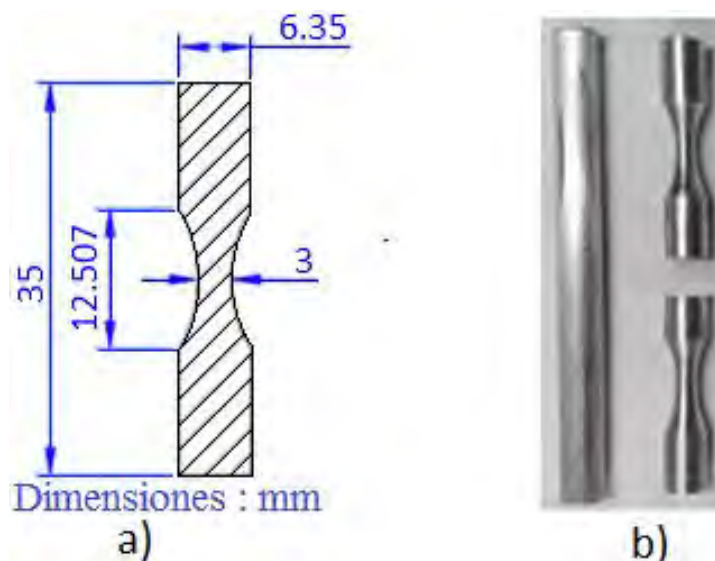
a) Dimensiones de la probeta de torsión (mm). b) Barra de aluminio original y probetas de fatiga por torsión mecanizadas.
